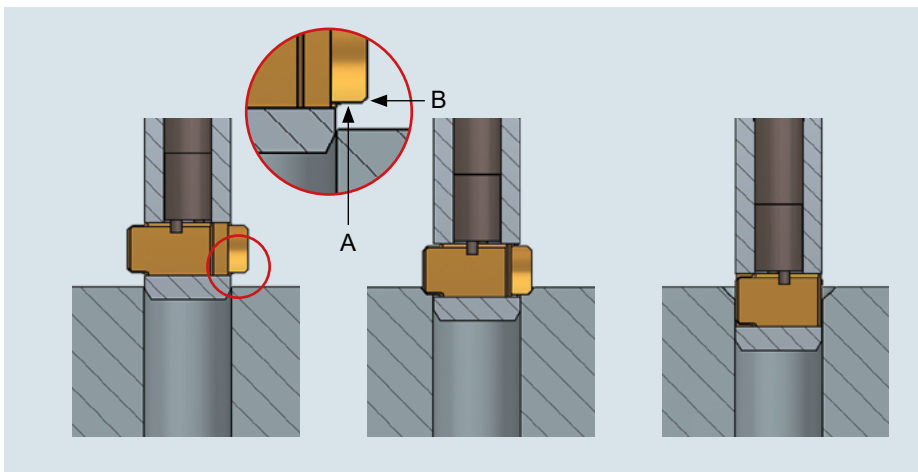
Funktionsprinzip DEFA-Werkzeug
